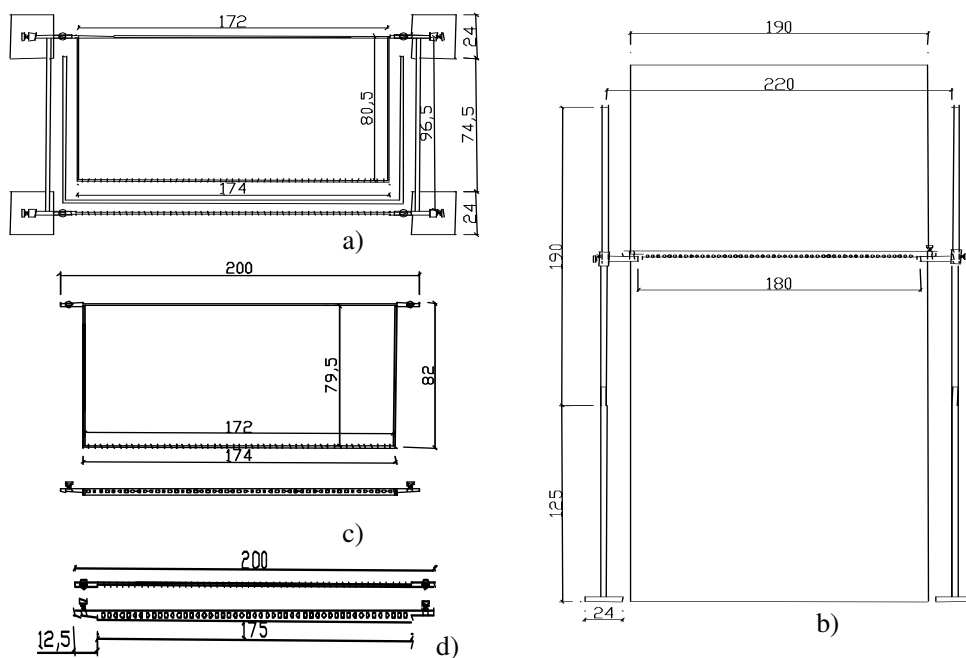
Supporto n.2 per il posizionamento del campione: a) pianta; b) prospetto; c) pianta e prospetto dell'asta orizzontale da posizionare sul fronte dell'accessorio; d) pianta e prospetto dell'asta orizzontale da posizionare sul retro dell'accessorio (quote in cm)
